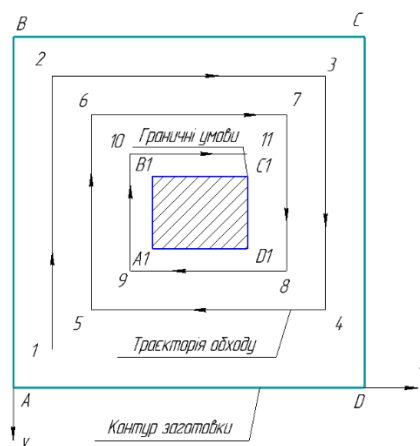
Траєкторія обходу механічної обробки заготовки
